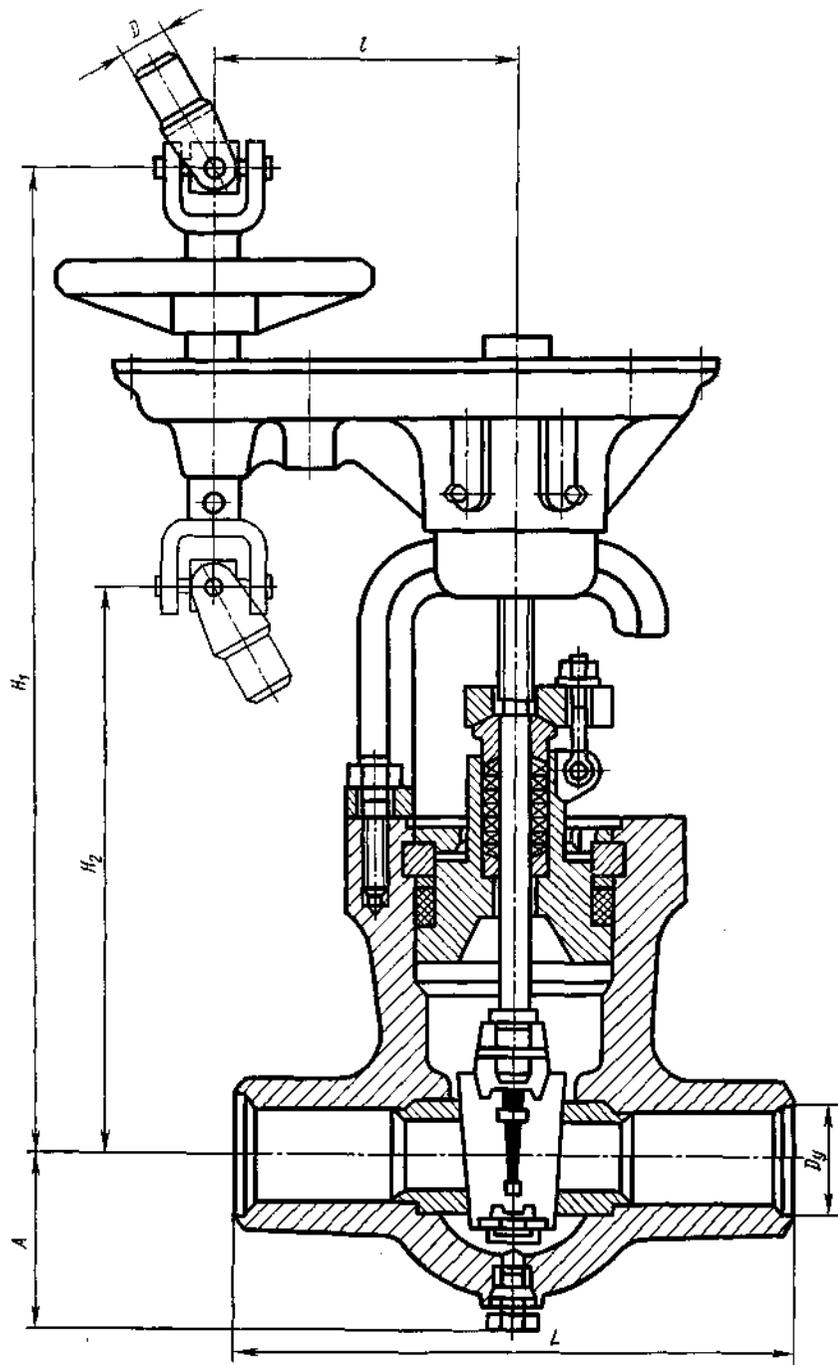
Задвижка с приводной головкой с цилиндрическим зубчатым редуктором Ду 100, 125, 150, 175, 200, 225, 250 и 300 серий 880 ... 883, 885 ... 887
